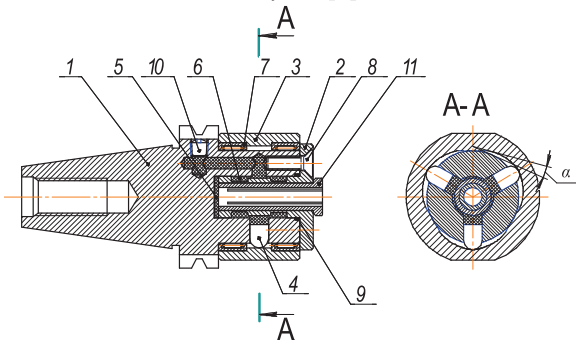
Конструктивна схема інструментального затискного патрона з гідропластом: 1 – корпус, 2 – циліндрична тонкостінна втулка, 3 – поворотна обойма, 4 – плунжер, 5 – фторопластова шайба, 6 – плинне середовище – гідропласт, 7 – голчастий підшипник, 8 – гвинт, 9 – фторонітова прокладка, 10 – пробка, 11 – цанга
